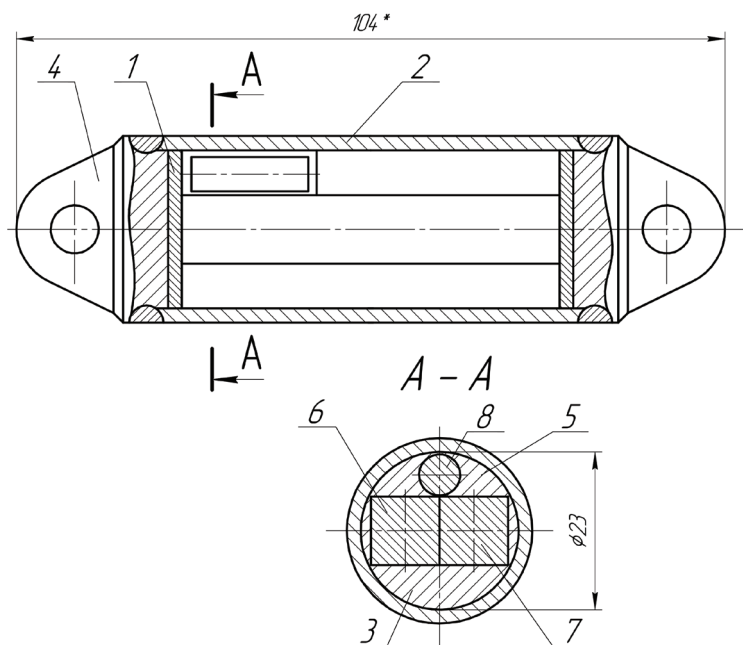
Стандартный контейнер с ударными образцами-свидетелями и индикатором флюенса нейтронов
